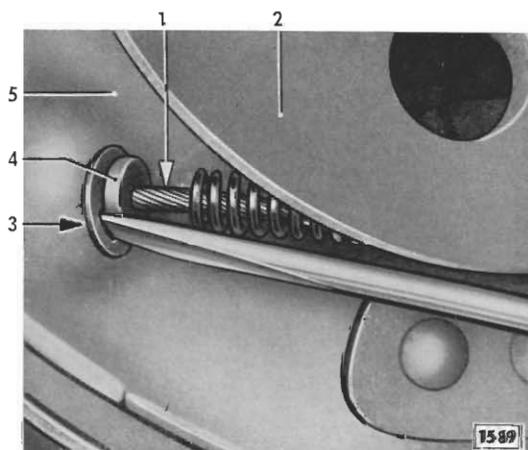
Sicherungsklammer von Bremsseilführungstülle abdrücken
